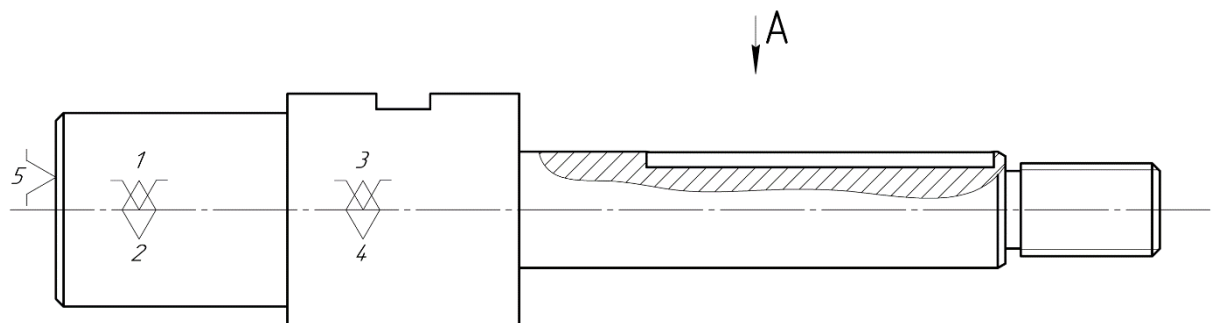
Принципиальная схема зажима заготовки в приспособлении с указанием мест приложения силы зажима.
